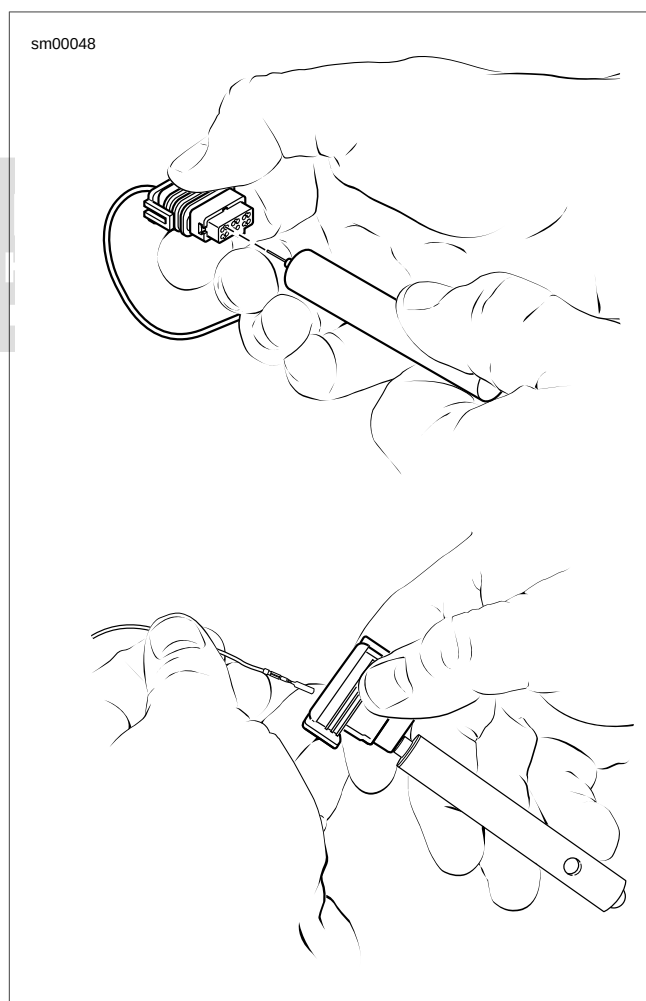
Conector Packard Micro 64: Inserción de la herramienta y extracción del terminal
